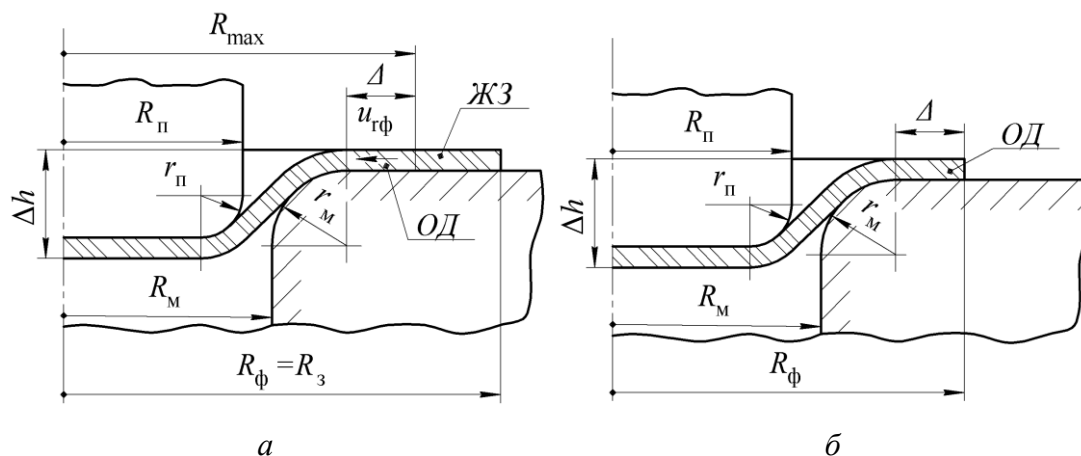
Схеми витягування вісесиметричних заготовок: *а* – «великої»; *б* – «малої»
